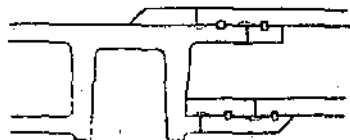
Способ сверления и вырезывания в несломанной части при сварке в месте смычки.
